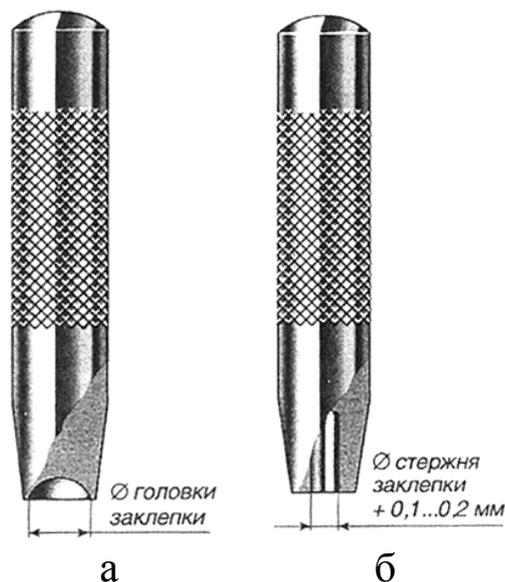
Приспособления для ручной клепки: а – обжимка; б – натяжка
